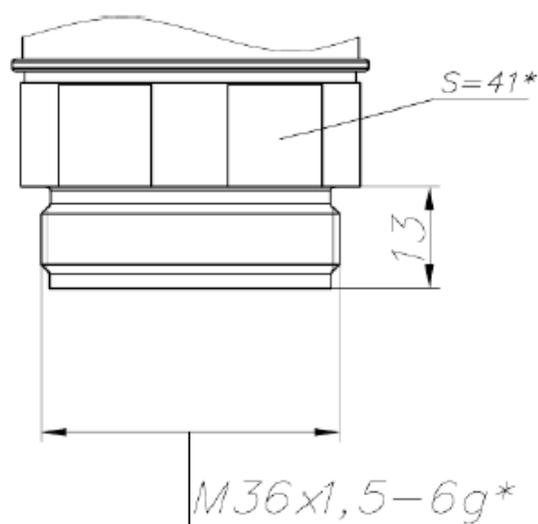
Габаритные размеры штуцера преобразователей с кодом соединительной части В
